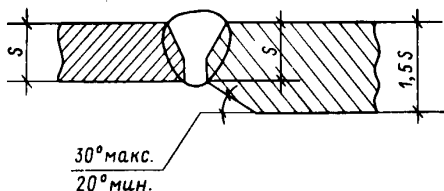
1. Конструктивные размеры разделки кромок и сварных швов разнотолщинных труб (до 1,5 толщины стенки)
